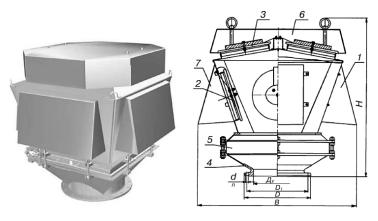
Дыхательный клапан КДС 1500/200. Изображение (слева) и общий вид (справа), [14]: 1 – корпус; 2 – тарелка вакуума; 3 – тарелка давления; 4 – переходник; 5 – кассета огневого предохранителя; 6 – крышка; 7 – воздуховод
